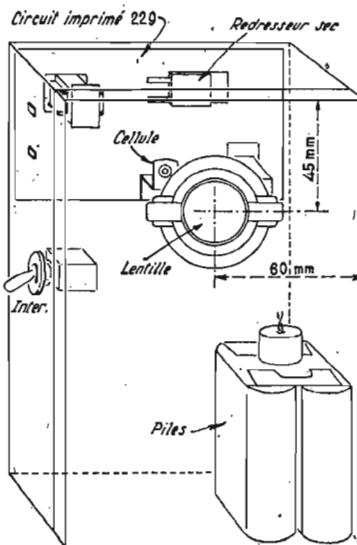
Disposition des éléments à l'intérieur du boîtier du récepteur. La lentille est fixée sur le couvercle
